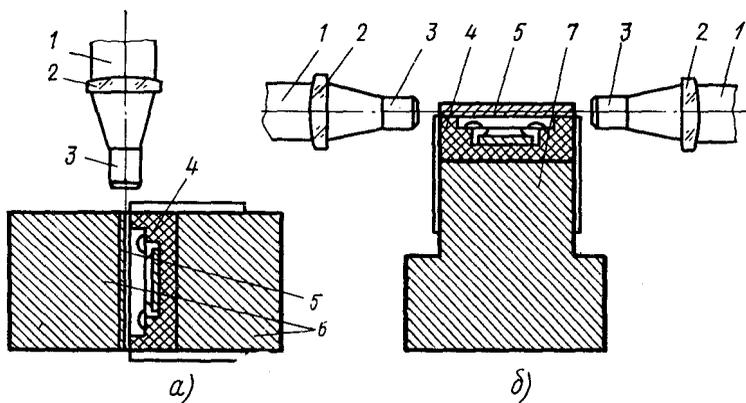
Схемы герметизации лазерной сваркой:
